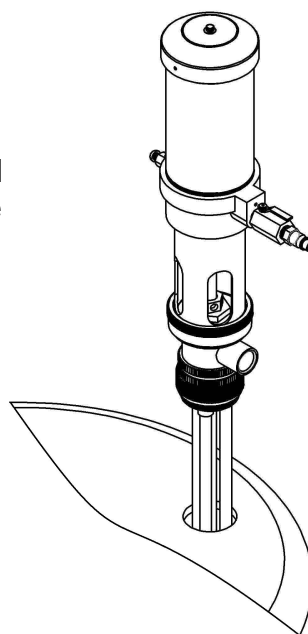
Figura B - Imagen de montaje instalación del equipo con bomba y mezclador de tambor.
